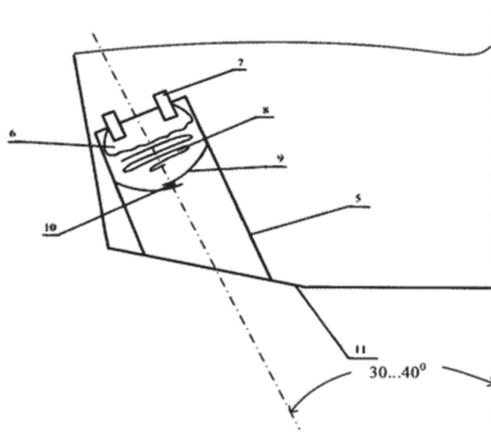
Вид контейнера с боковой подушкой и сеткой: 5 – прямоугольный корпус; 6 – подушка безопасности; 7 – пиропатроны; 8 – сетка; 9 – боковые эластичные створки; 10 – соединительные липучки; 11 – бампер
